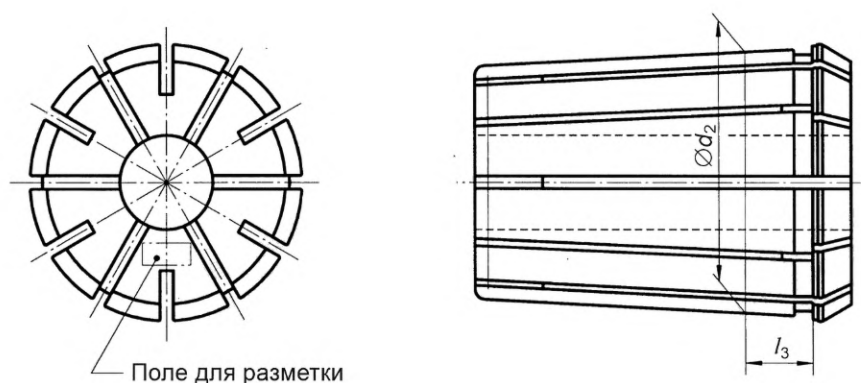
Цанга формы В с двусторонними прорезями и непрерывным зажимным отверстием для цилиндрических хвостовиков
